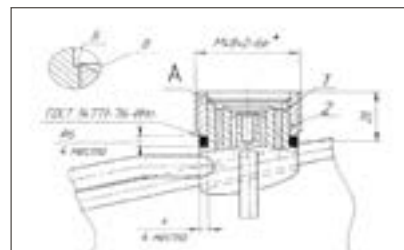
Схема ремонта фланцев патрубков впуска топлива:
